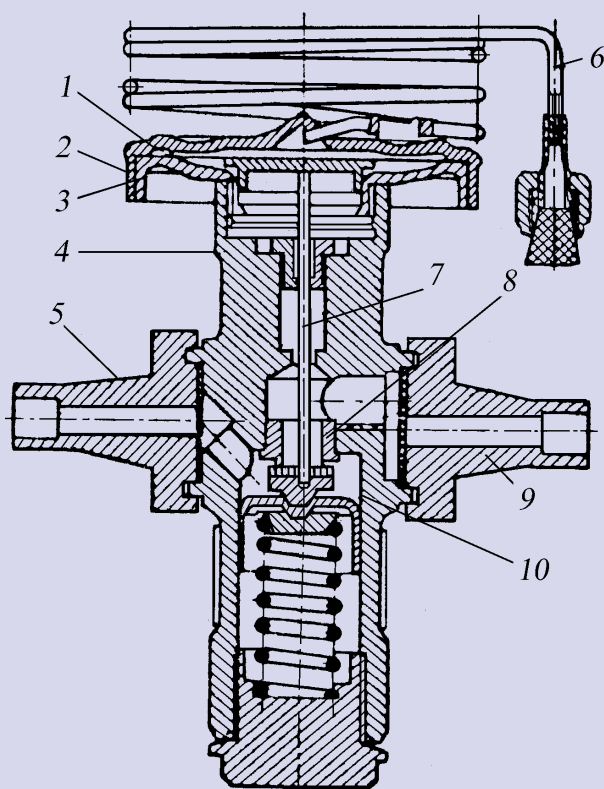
Клапан подачи жидкого азота: 1 — мембрана; 2 — верхняя крышка; 3 — нижняя крышка; 4 — корпус; 5, 9 — фланец; 6 — импульсный трубопровод; 7 — шток; 8 — седло; 10 — клапан
